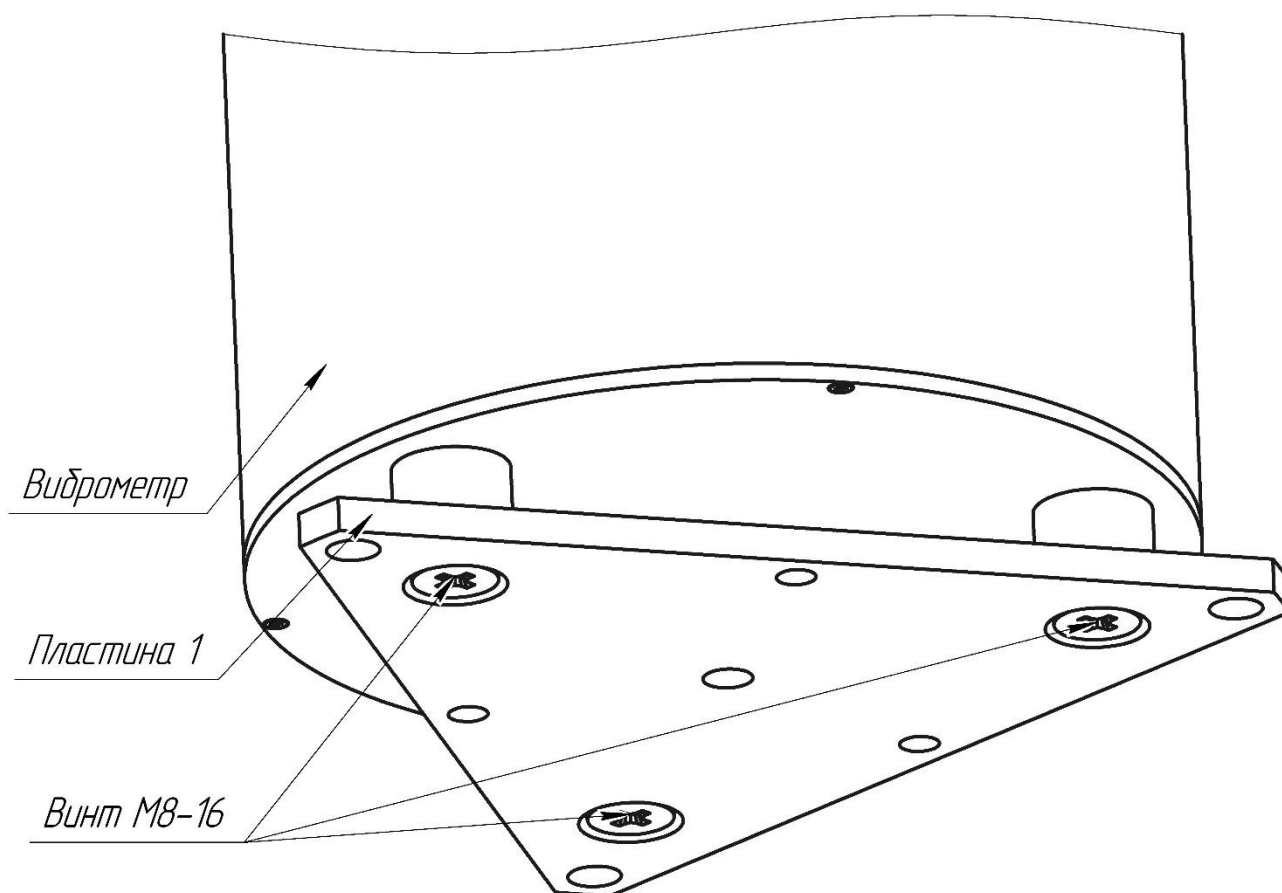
Крепление виброметра без регулировки – Шаг 1
